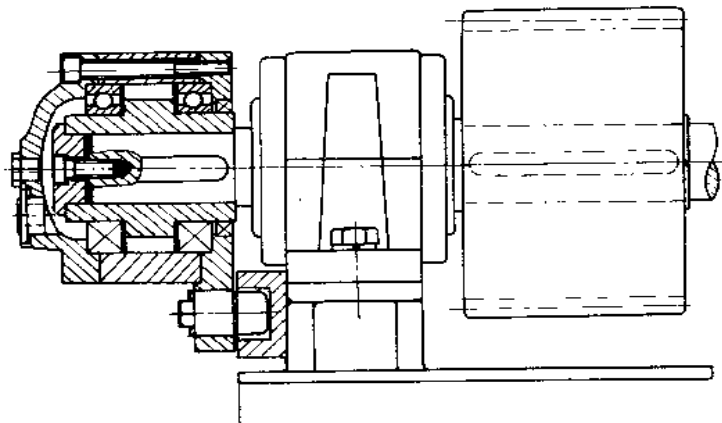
棘爪型超越离合器用在大的小齿轮轴上
